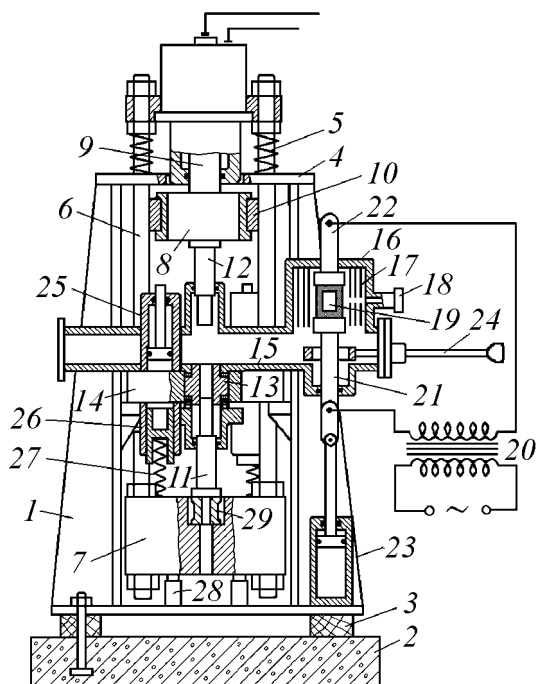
Блок-схема экспериментальной установки для горячей динамической прессовки: 1 – станина; 2 – фундамент; 3 – прокладка; 4 – поперечина; 5 – пружина; 6 – колонка; 7 – шабот; 8 – баба; 9 – рабочий шток; 10 – направляющая; 11, 12 – соответственно нижний и верхний пуансонодержатели; 13 – матрица; 14 – матричная плита; 15, 16 – соответственно вакуумная и нагревательная камеры; 17 – теплозащитные экраны; 18 – смотровое окно; 19 – образец; 20 – понижающий трансформатор; 21, 22 – соответственно нижний и верхний токовводы; 23 – пневмоцилиндр; 24 – толкатель; 25, 26 – соответственно верхний и нижний гидроцилиндры; 27 – пружина; 28 – упор
